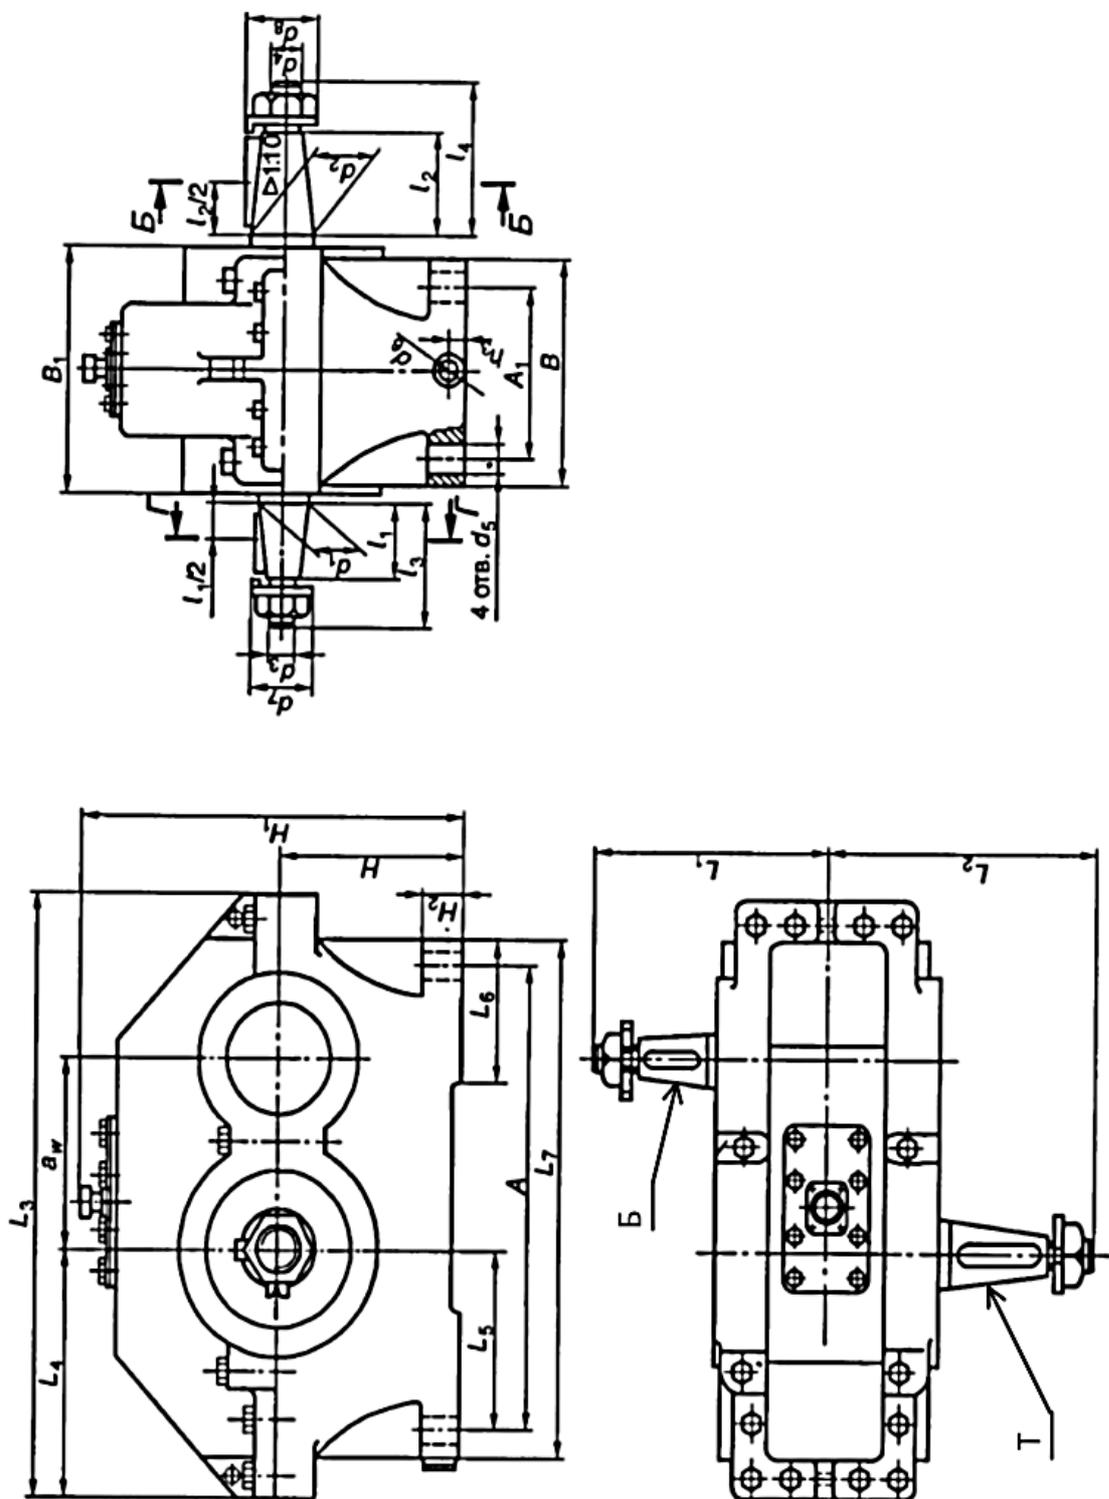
Габаритные и присоединительные размеры цилиндрических редукторов типа ЦУ:
